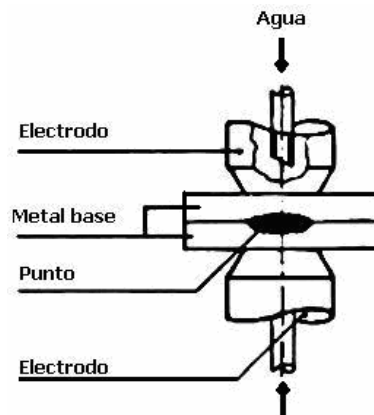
Esquema del proceso de soldadura por resistencia aplicado al fleje metálico
